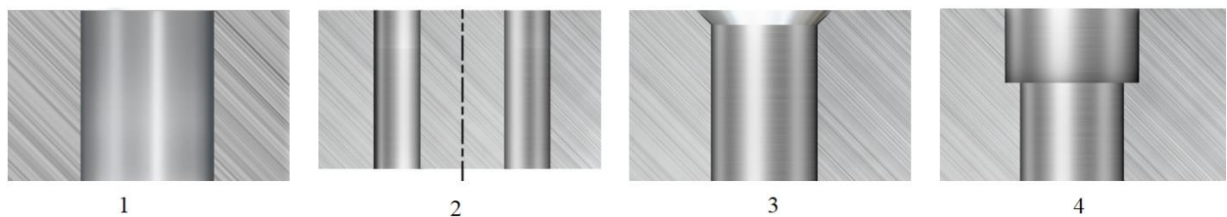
Методи свердління отворів: 1 – звичайне свердління; 2 – корончасте свердління; 3 – свердління з фаскою; 4 – свердління ступінчастих отворів
